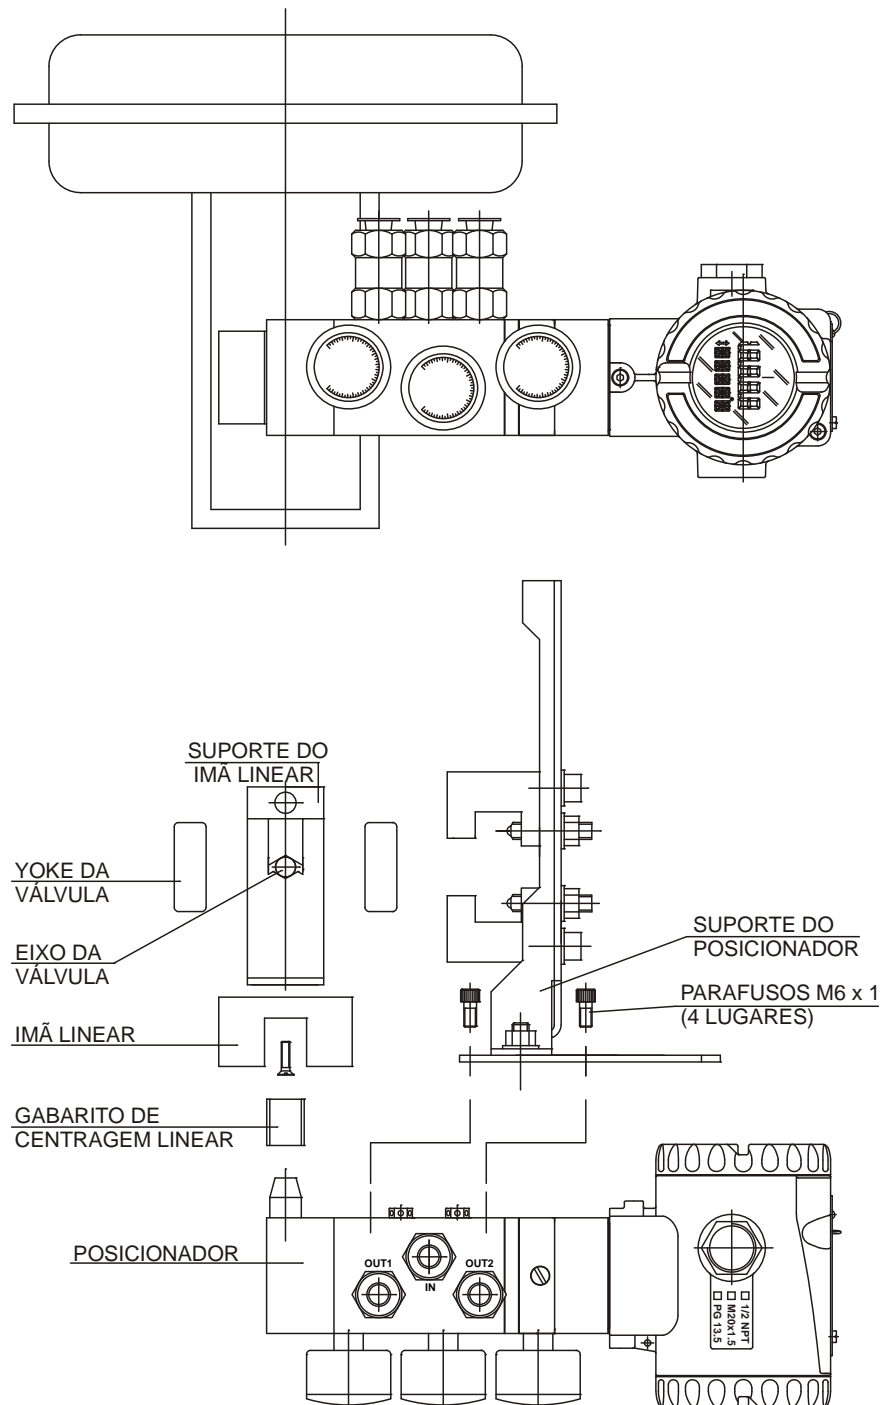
Esquema de Montagem do Posicionador em Atuador Linear
